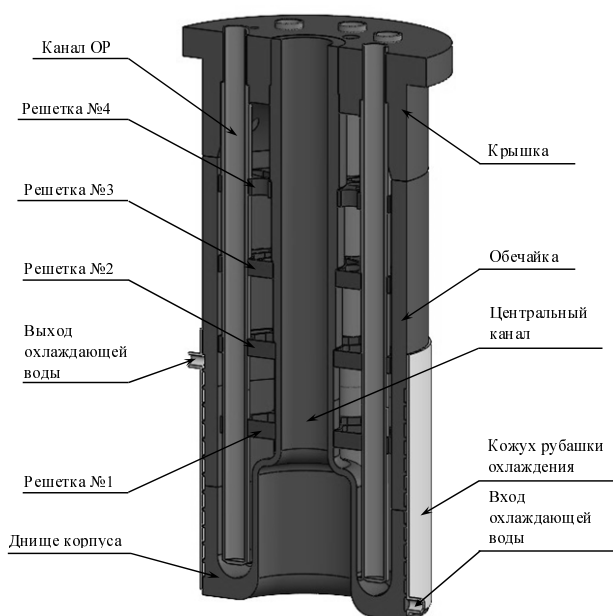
Конструктивная схема корпуса АЗ реактора ВИР-3
